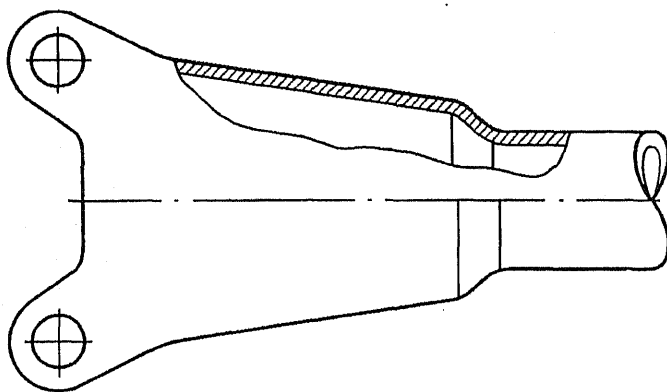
Стыковочный узел лопасти вертолета Ми-26
